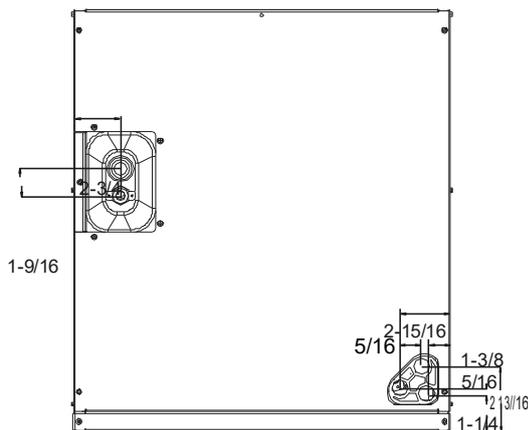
DIMENSIONES DE LA CONEXIÓN FRONTAL DEL SERPENTÍN
